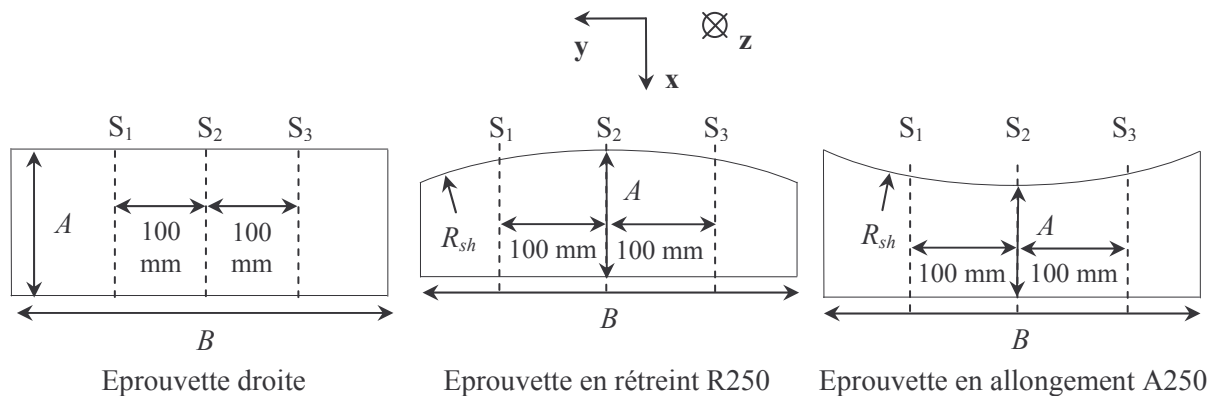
Géométries des flans usinés pour chaque éprouvette étudiée, sections de mesure et sens de laminage.
